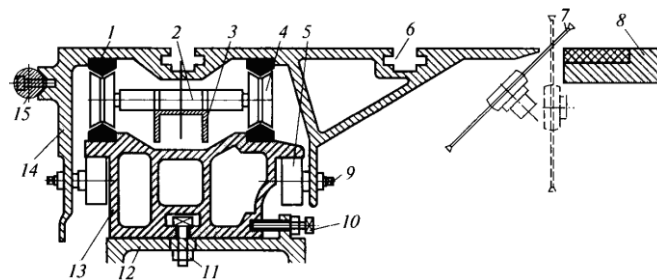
Пристрій основної каретки: 1 – напрямна; 2 – вісь; 3 – візок; 4 – базувальний ролик; 5 – притискний ролик; 6 – паз; 7 – пилка; 8 – стіл верстата; 9 – ексцентрикова вісь; 10 – регулювальний гвинт; 11 – гайка; 12 – станина; 13 – основа каретки; 14 – корпус каретки; 15 – напрямна додаткової каретки
